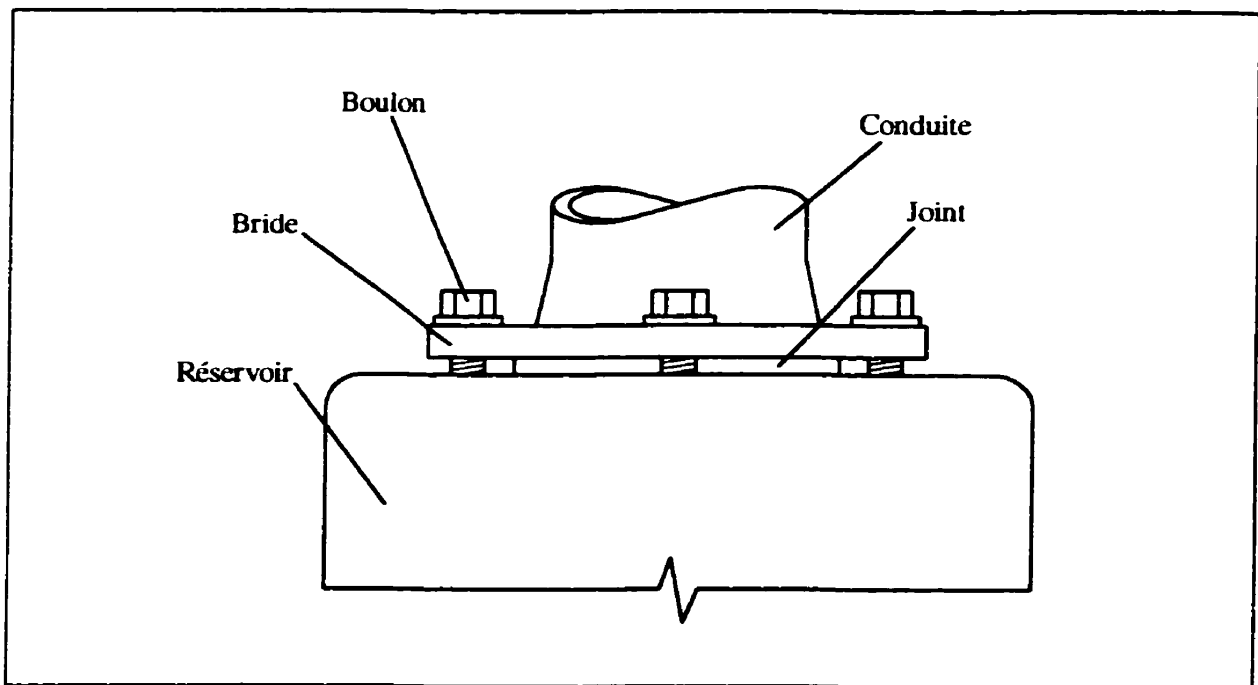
Exemple de raccord avec joint d'étanchéité entre une conduite et un réservoir
